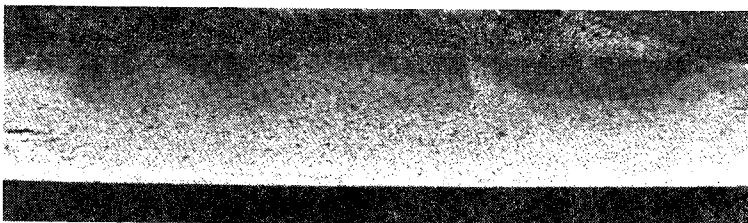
変動ブロック荷重による破断面の状況 (文献8)
